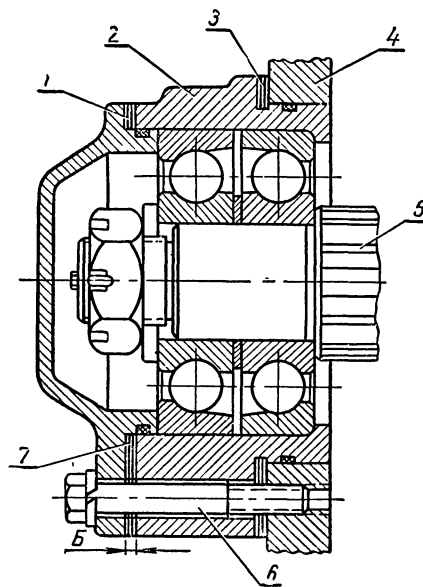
а. Схема регулировки осевого люфта подшипников на переднем конце вторичного вала трактора Т-75:
